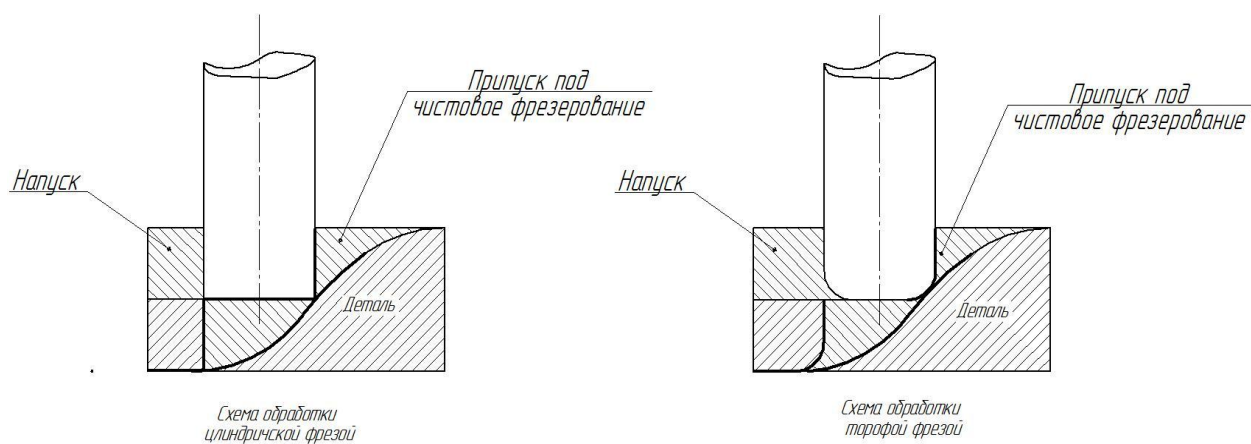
Послойное снятие напуска при черновом фрезеровании цилиндрической и торовой фрезой
